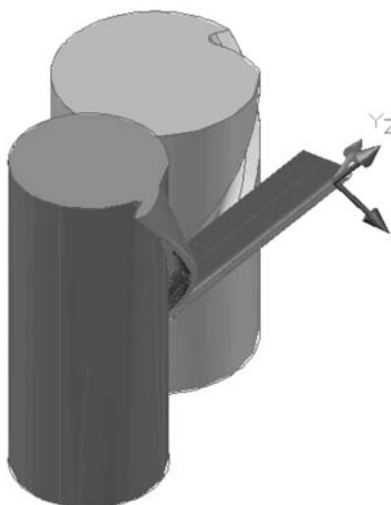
Твёрдотельные модели детали с ВП и червячной фрезы:
